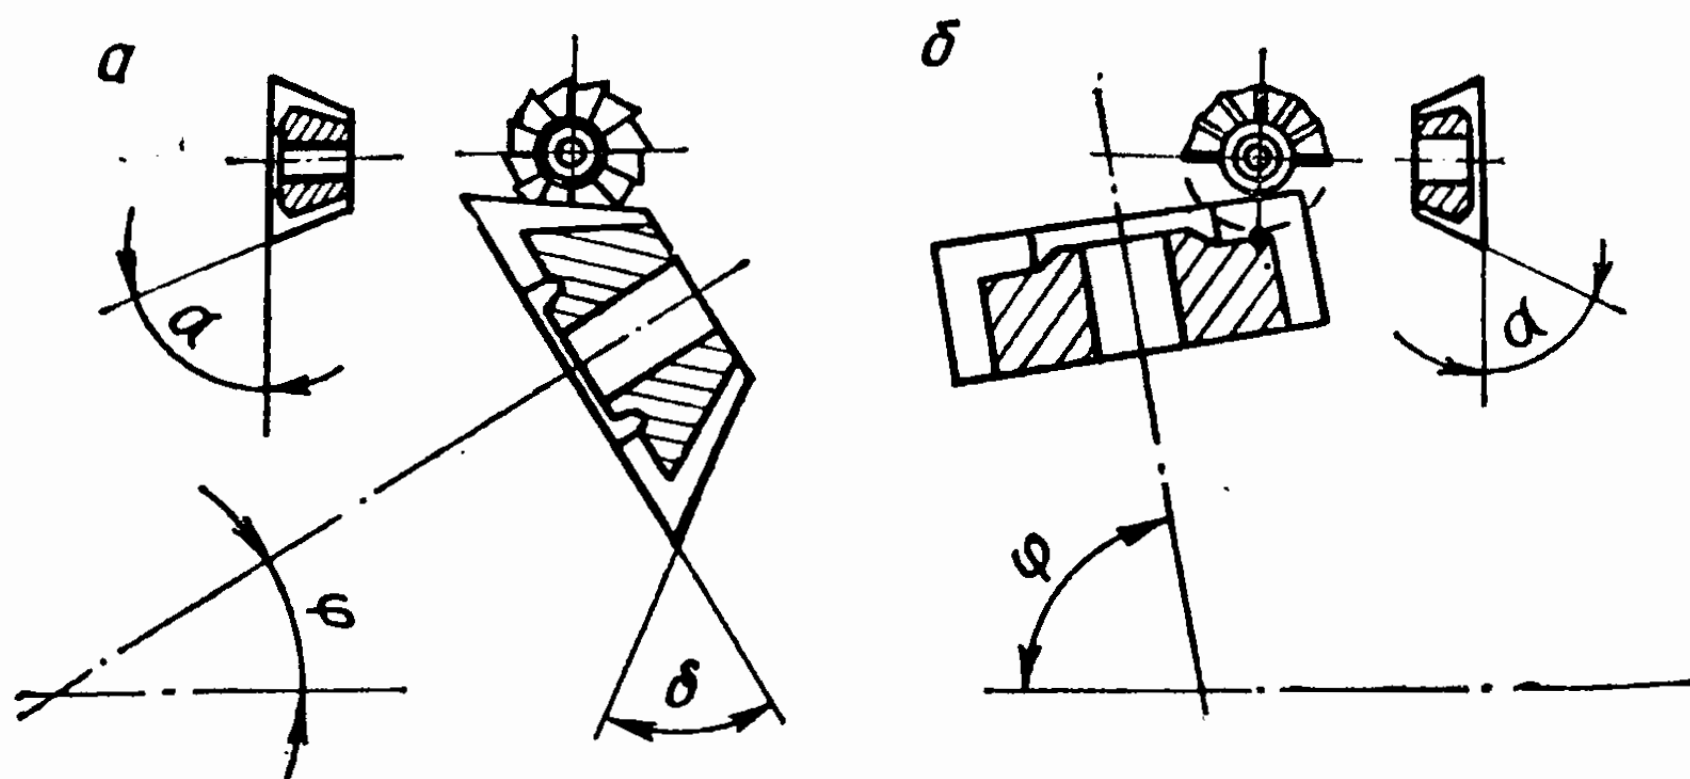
Положение оси шпинделя УДГ и заготовки при фрезеровании канавок на конусе и торце.
